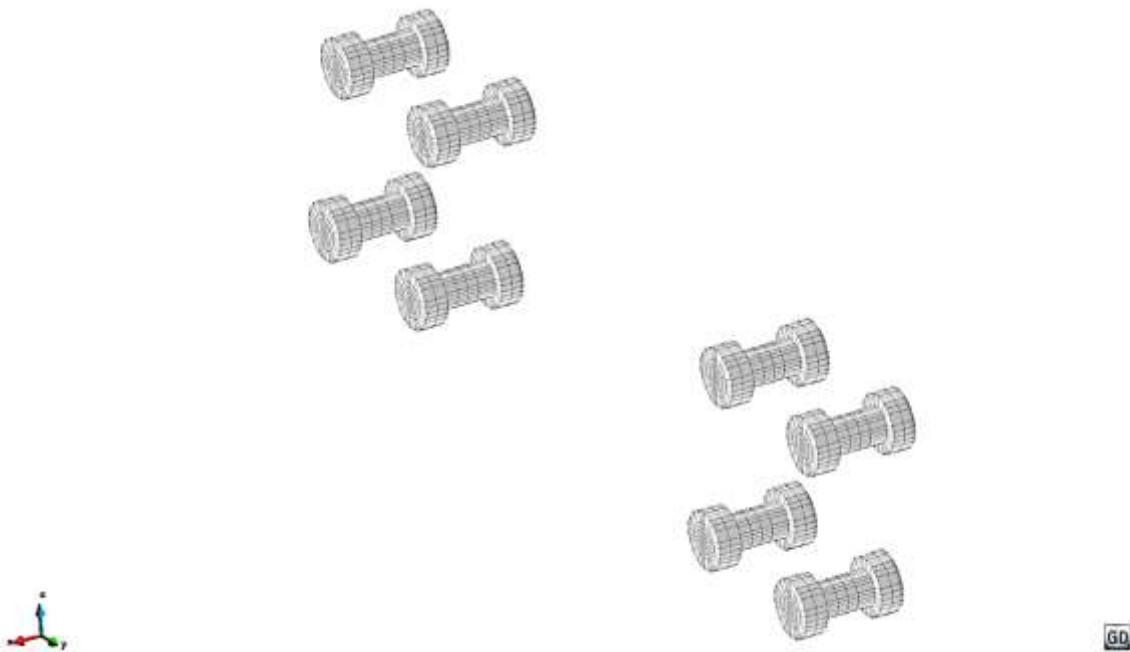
Mallado generado para la tornillería en la conexión. (GID 11.1.8).
